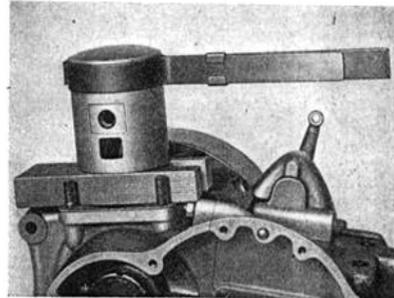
Anwendung der Kolbenringklammer Nr. 0966 und einer Holzgabel als Auflage für den Kolben beim Aufsetzen des Zylinders
